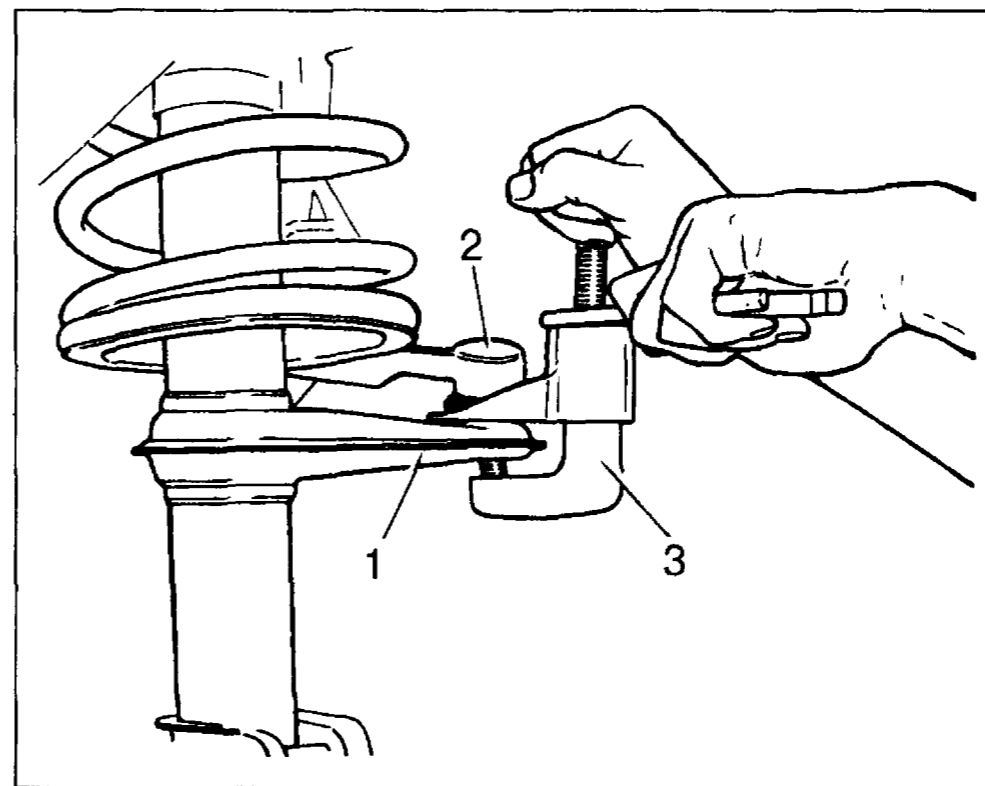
Выпрессовка пальца шарового шарнира рулевой тяги из поворотного рычага стойки подвески: 1 — поворотный рычаг; 2 — шаровой шарнир тяги; 3 — съемник А.47035
